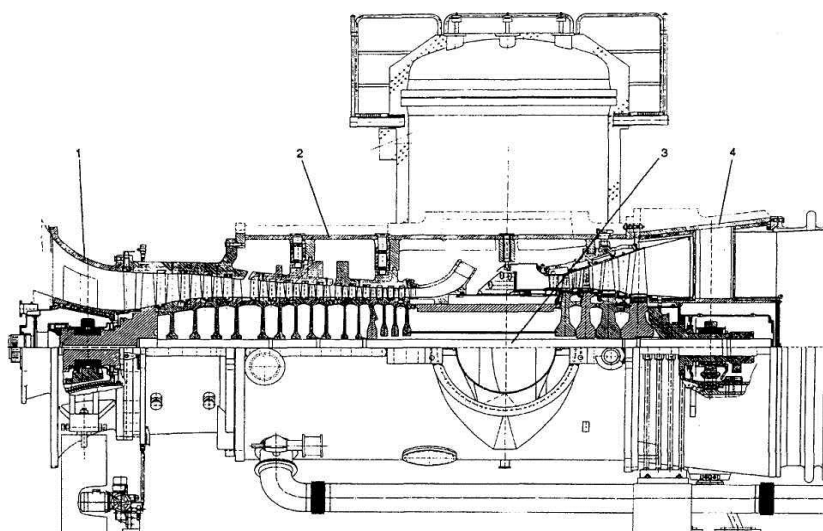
Продольный разрез ГТЭ-160: 1 – стойка переднего подшипника; 2 – корпус; 3 – ротор; 4 – выхлопной патрубок с задним подшипником
